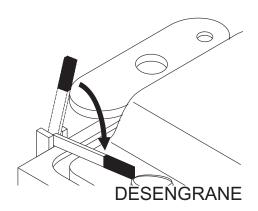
Palanca de transmisión de engrane/desengrane (posición de desengrane)
